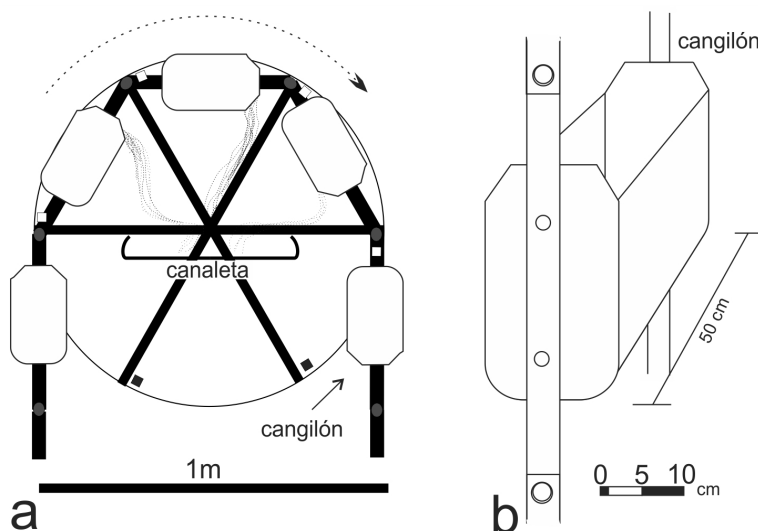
a: Vista corte longitudinal de la cadena de cangilones; b: Esquema de un cangilón con su eslabón.
